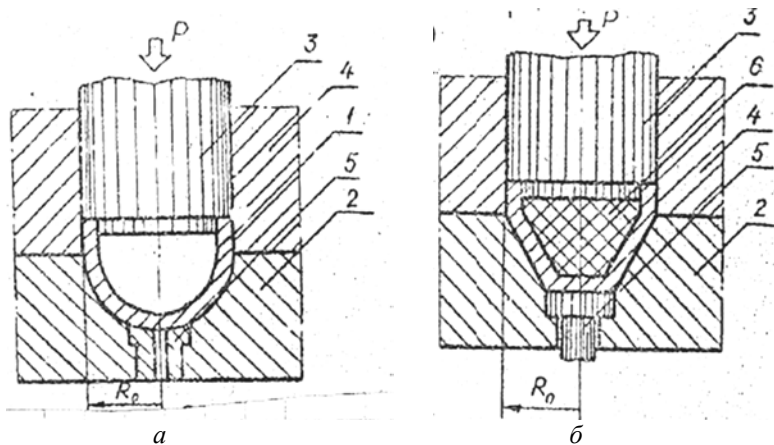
Схемы обжима полых заготовок с дном в полусферической (а) и конической (б) матрицах: 1 – заготовка; 2 – матрица; 3 – пуансон; 4 – наружный подпор; 5 – выталкиватель; 6 – эластичный внутренний подпор
